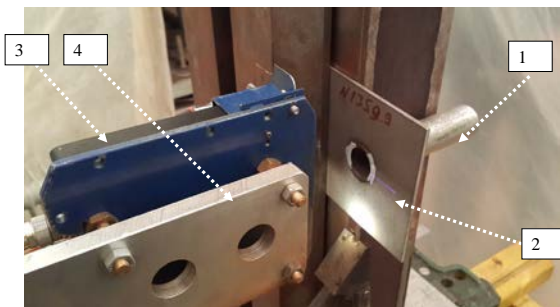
Положення макетного зразка системи пошуку місця зварювання, закріпленого на лабораторному стенді для лазерного зварювання: 1 – зразок, що зварюється; 2 – лінія, згенерована датчиком RiftekRF625; 3 – датчик RiftekRF625; 4 – кронштейни системи кріплення
